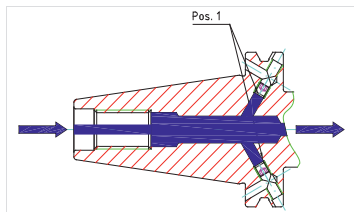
Kühlmittelzuführung Form AD/JD
